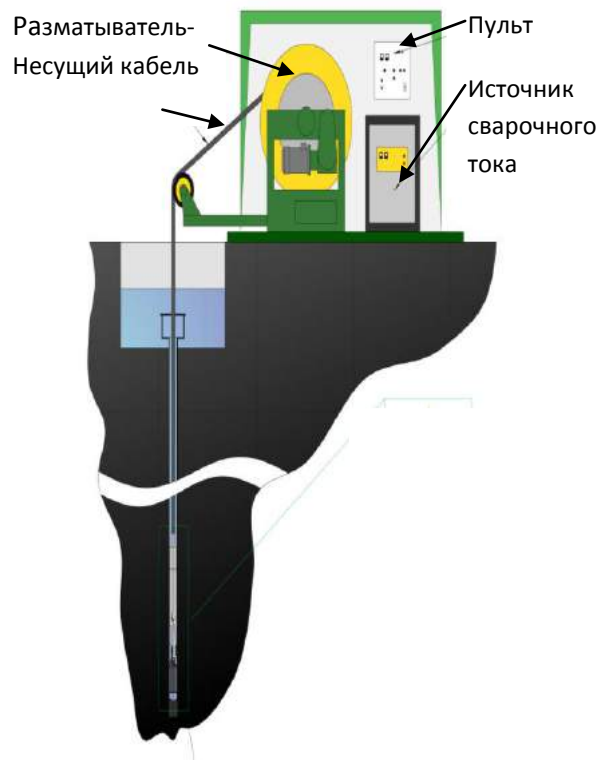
Полный комплекс автомата для глубоководной подводной сварки мокрым способом
